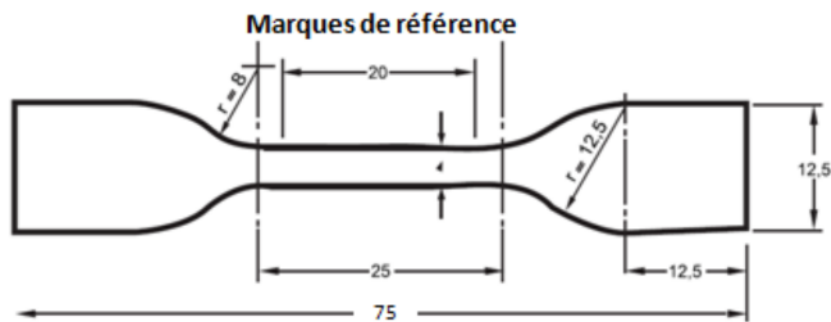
Dimensions d'une éprouvette sous forme d'haltère [37].
